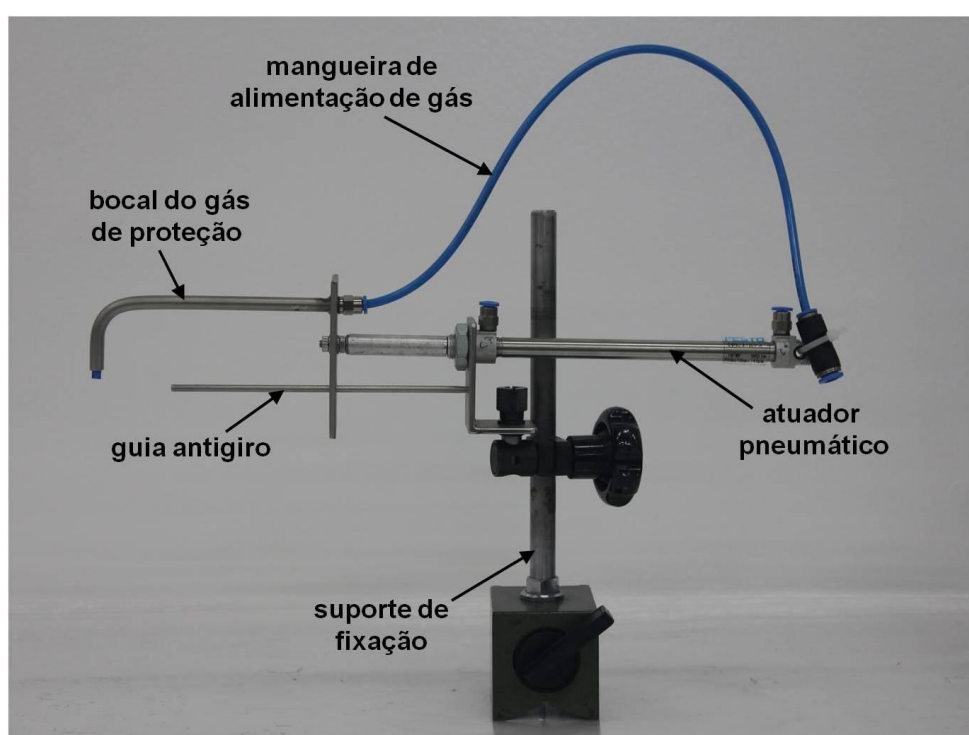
Arranjo do bocal do gás de proteção utilizado no sistema de soldagem a laser
